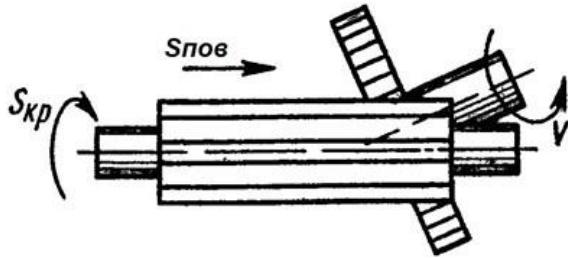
Зняття задирок на зубофрезерному верстаті
